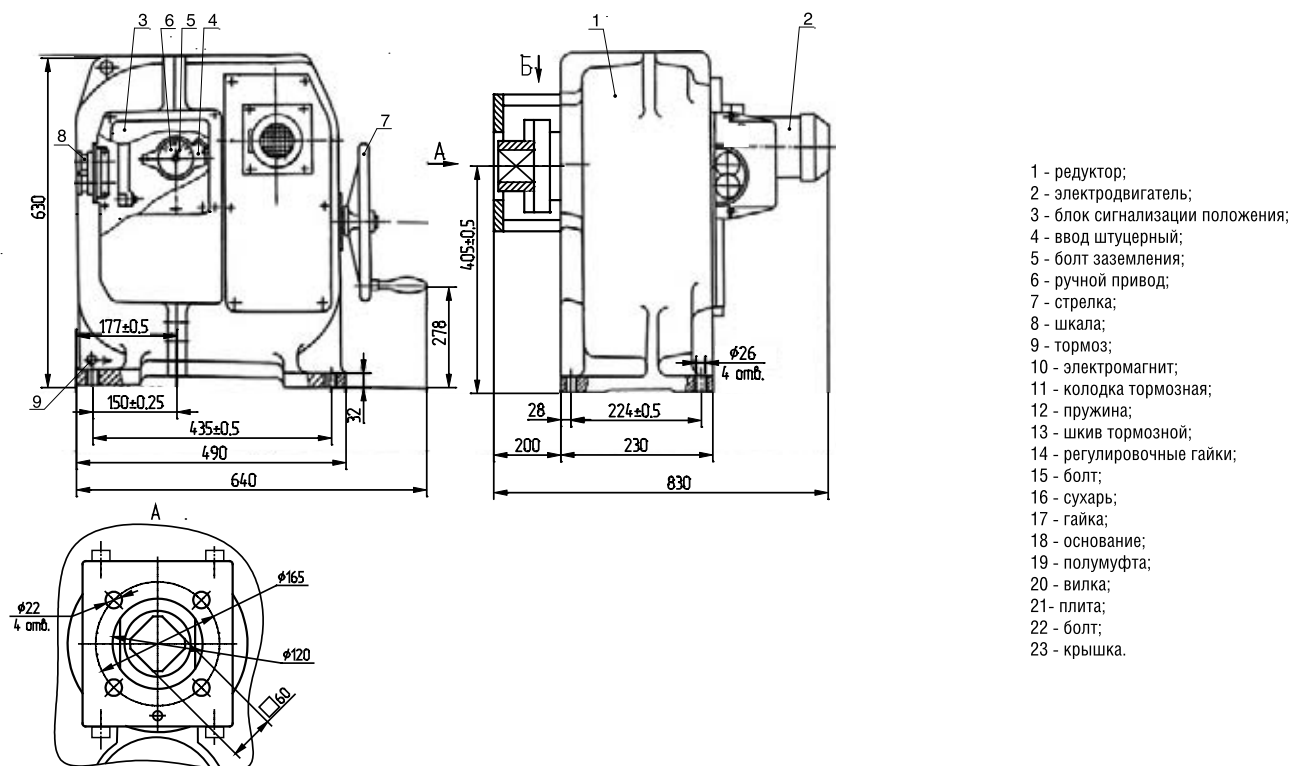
Габаритные и присоединительные размеры М30Ф-4000
